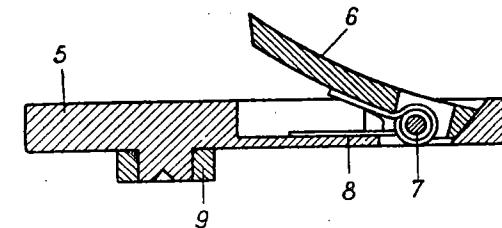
Ползун с подавателем в разрезе (сб. 34):
